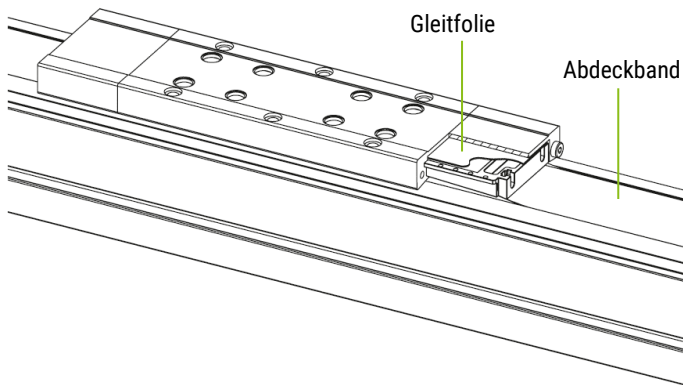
Demontage/Montage des Schlittenendstücks
